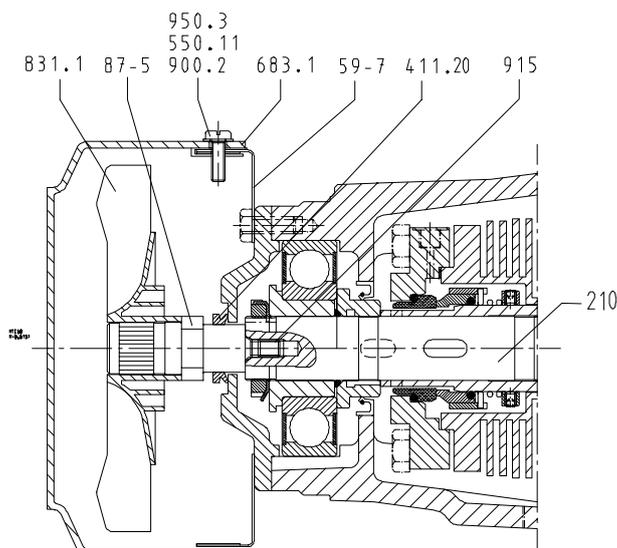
Smontaggio della tenuta meccanica refrigerata ad aria - fasi di smontaggio aggiuntive
